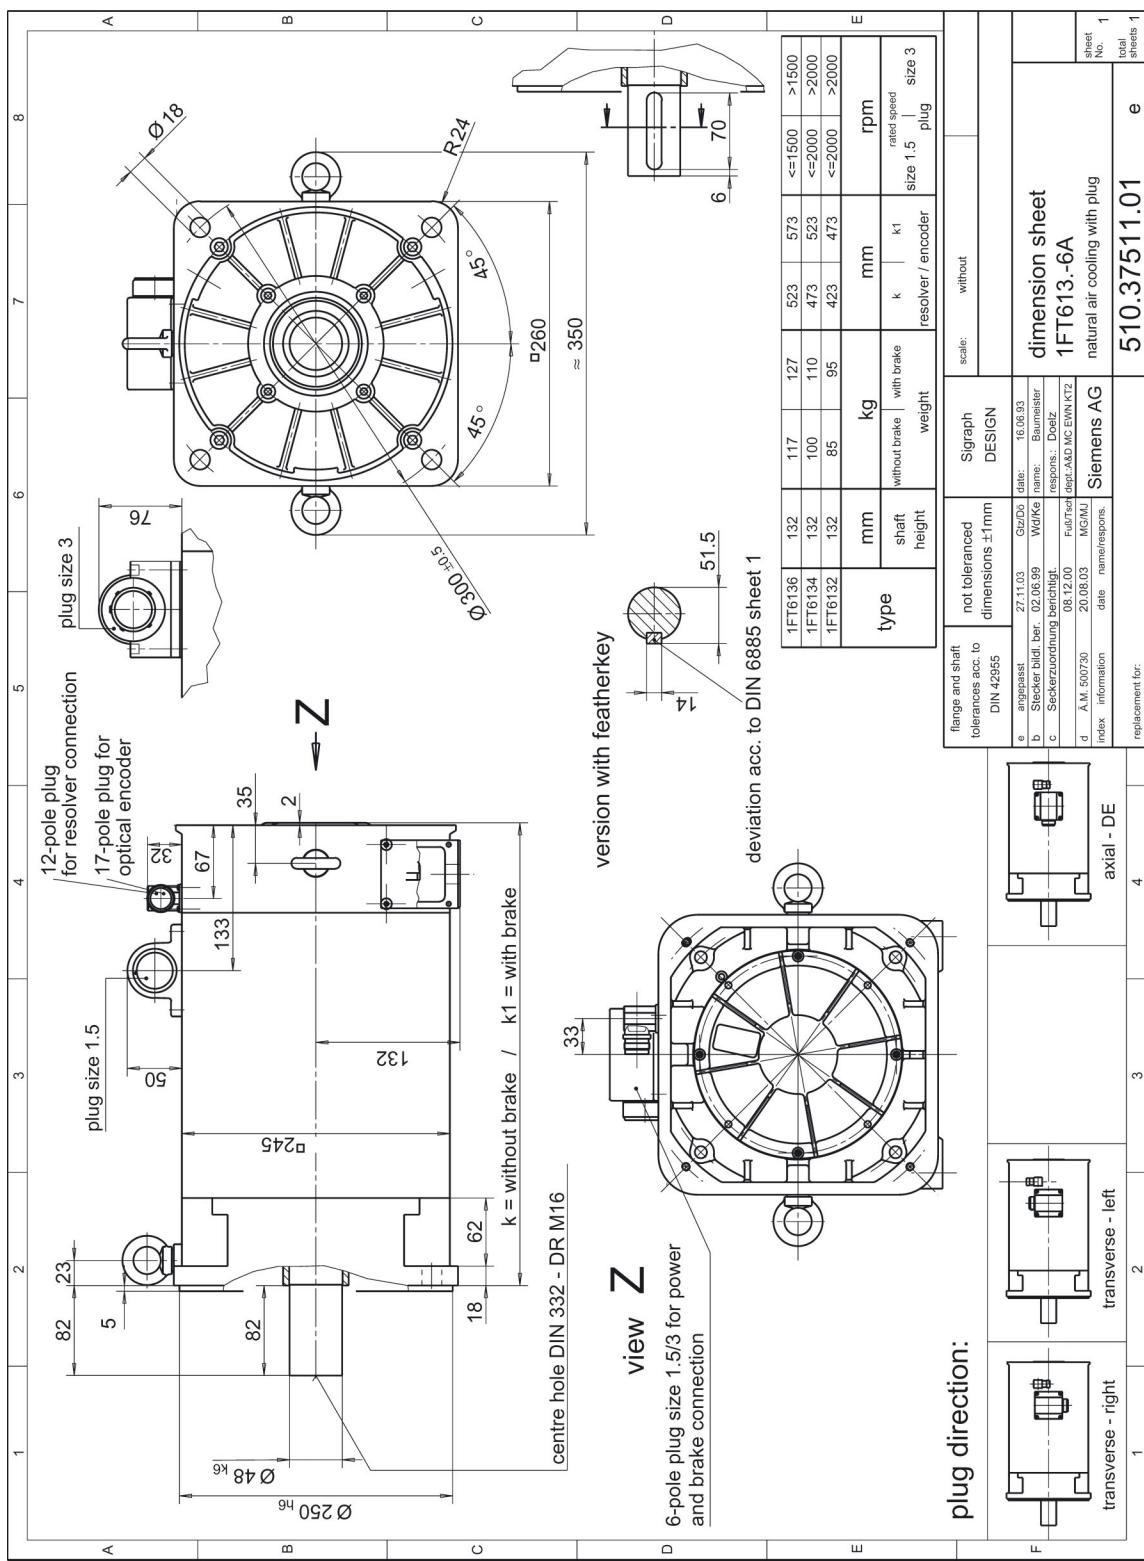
1FT613□ selbstgekühlt mit Stecker Größe 1.5/3
